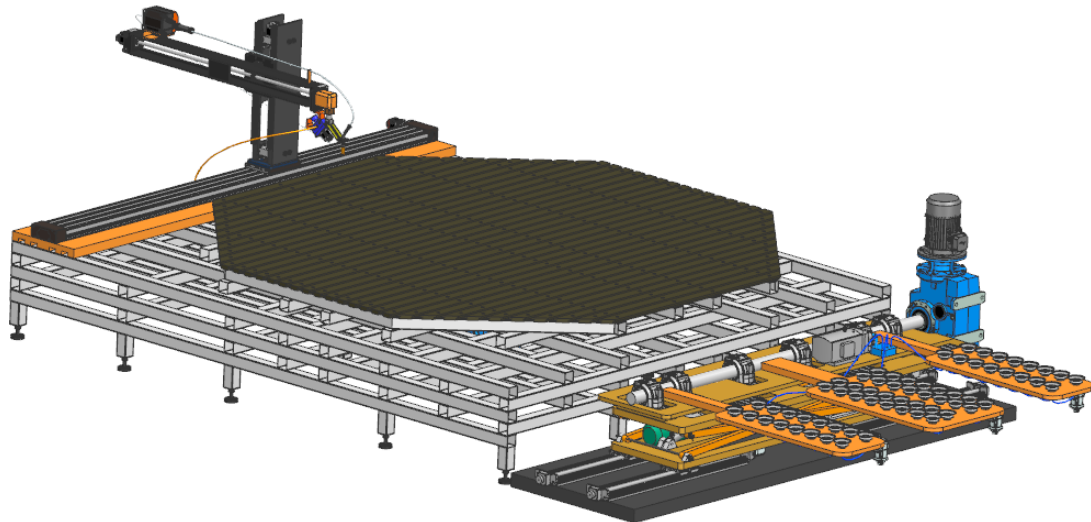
Электронный макет автоматической сварочной машины
